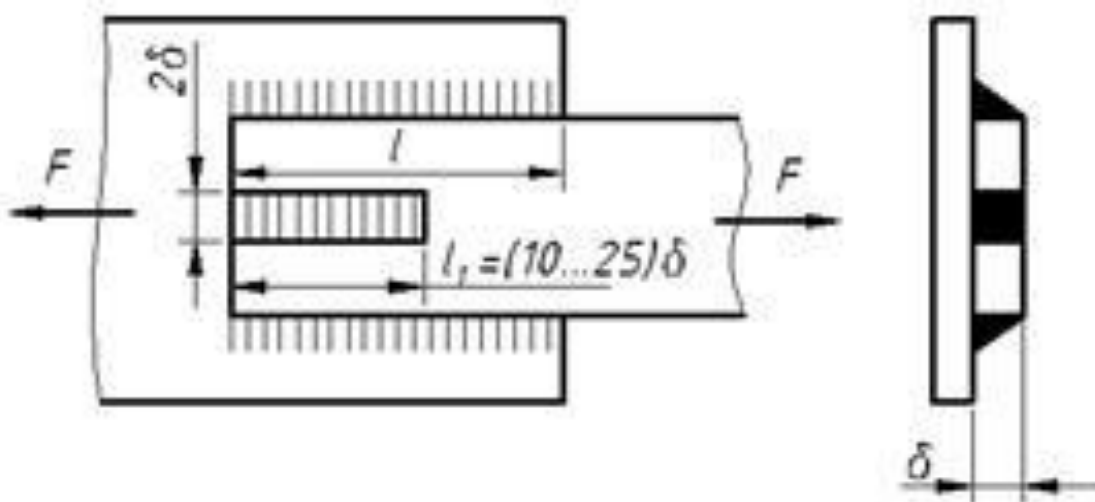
Расчет флангового сварного шва, усиленного прорезным сварным швом
